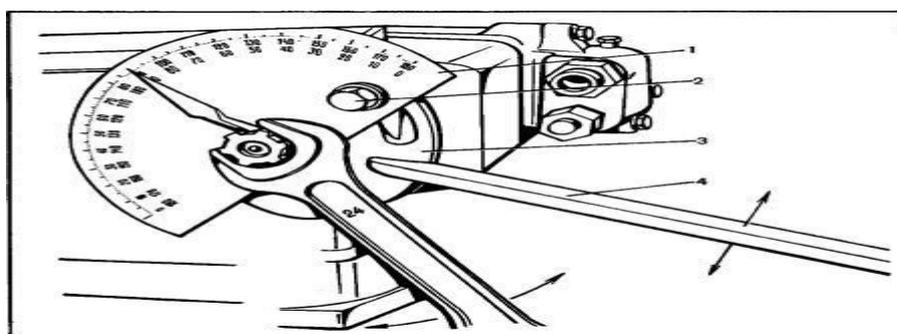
Регулировка свободного хода вала гидроусилителя руля (ГУР) тракторов МТЗ-80, МТЗ-82, 1 — лимб-транспортер; 2— болт; 3— эксцентриковая втулка; 4— монтировочная лопатка
